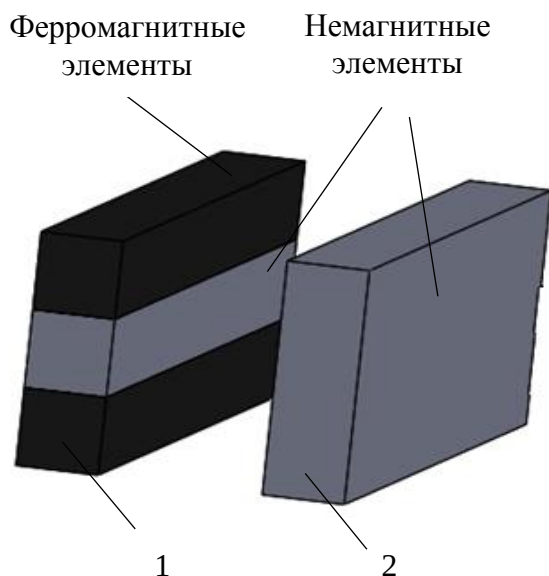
Конструкции поршня ЭМЖД: 1 – поршень с ферромагнитными элементами, 2 – немагнитный поршень
